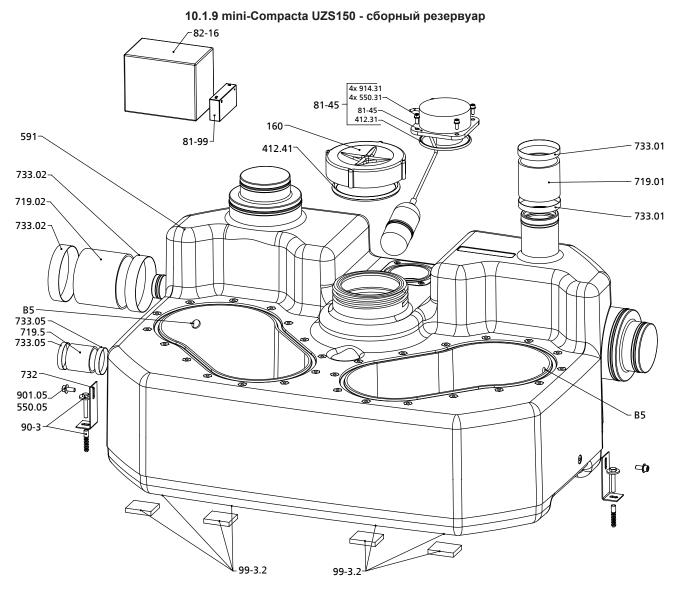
Покомпонентный сборочный чертеж mini-Compacta UZS 150 — сборный резервуар
